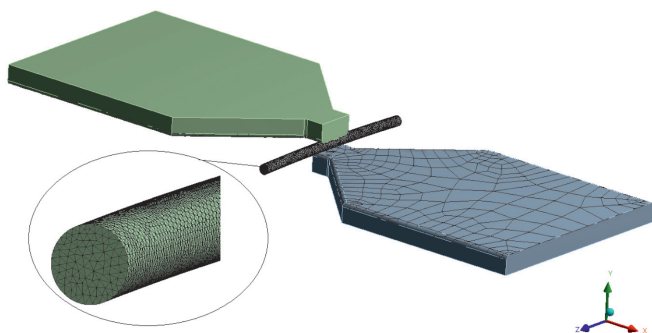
Конечно-элементная модель процесса правки и упрочнения искривленной цилиндрической детали
